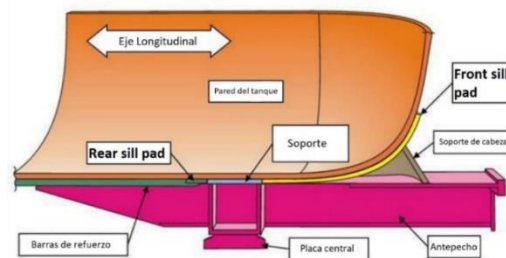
; Vista esquemática en corte del extremo del carrotanque que muestra los componentes principales.
